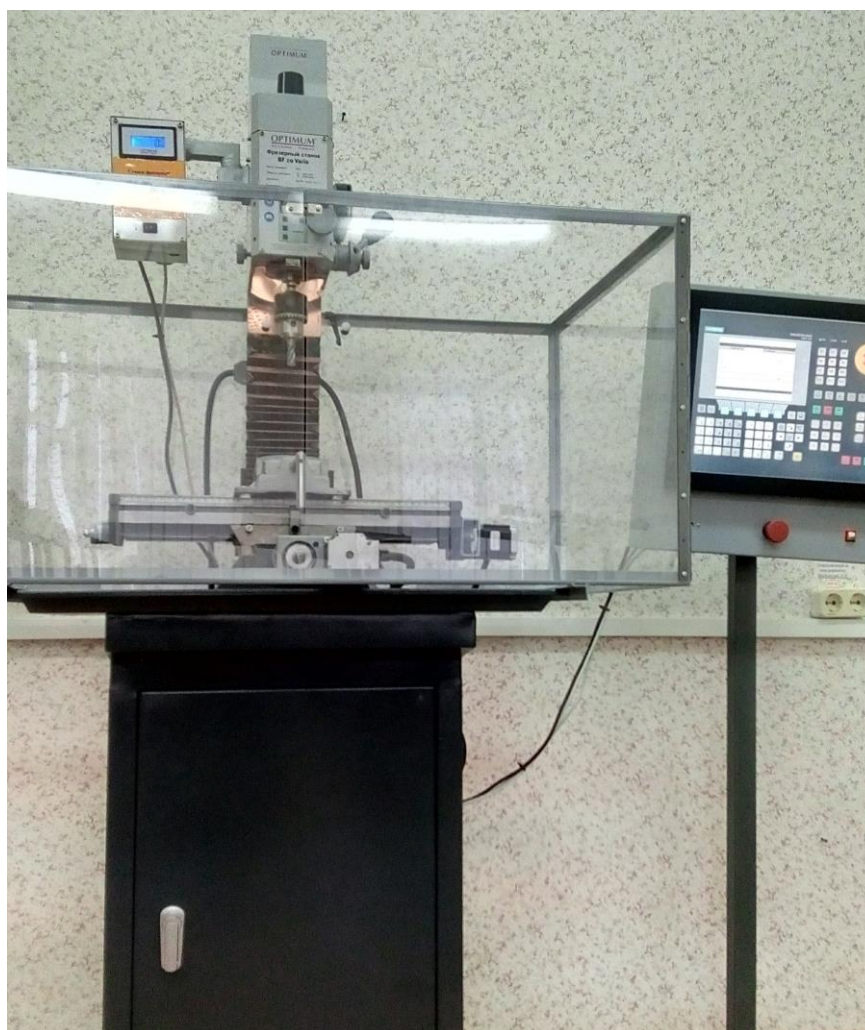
Фрезерный станок с ЧПУ Омега Ф3Ф-ВФ20
